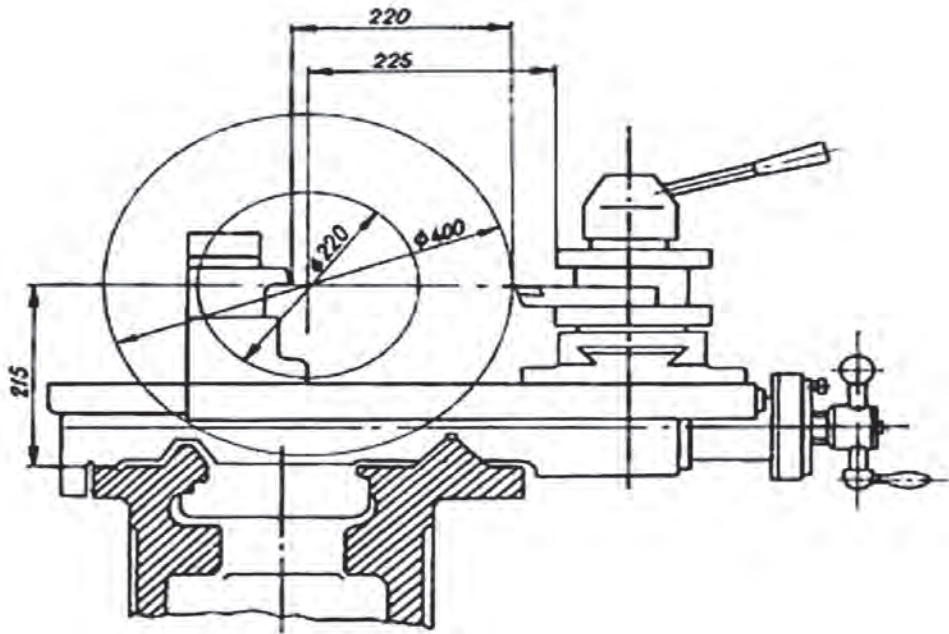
Ескіз супорту токарного верстата 16K20
